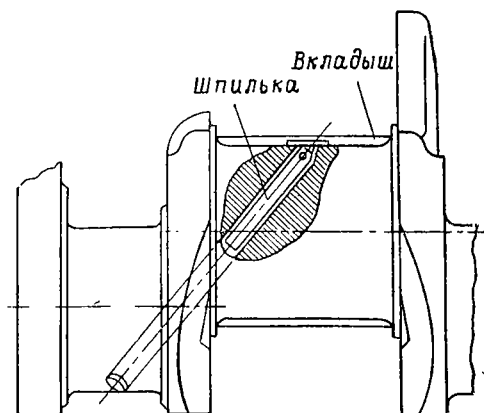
Установка шпильки в отверстие коренной шейки коленчатого вала
